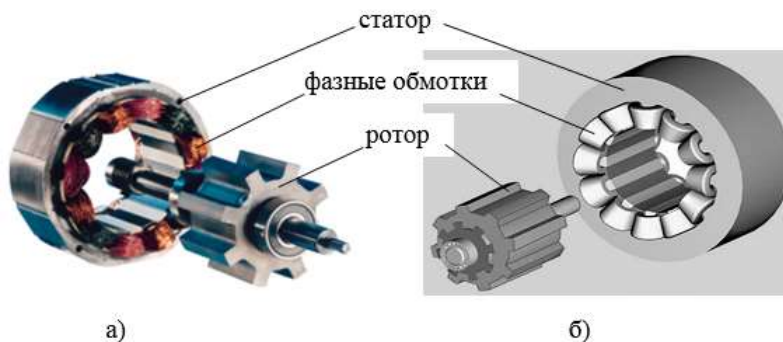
Статор и ротор вентильно-индукторного двигателя
